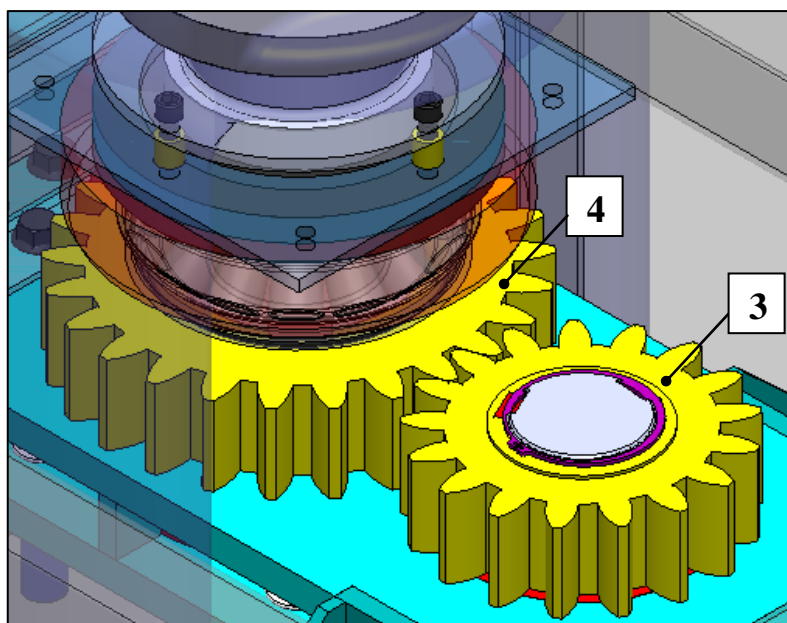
Representação de vista esquemática do pinhão 3 montado no equipamento HPT sob a condição de balanço
